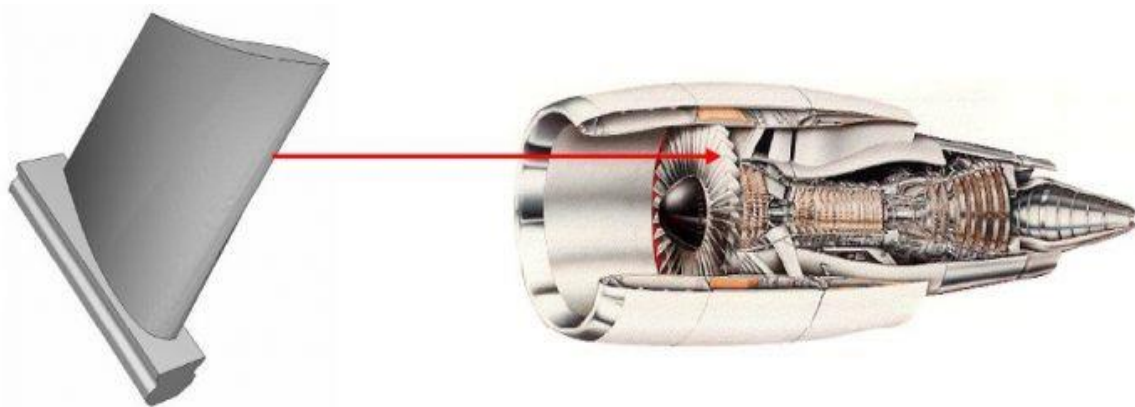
Використання лопатки з титанового сплаву в газотурбінному двигуні
